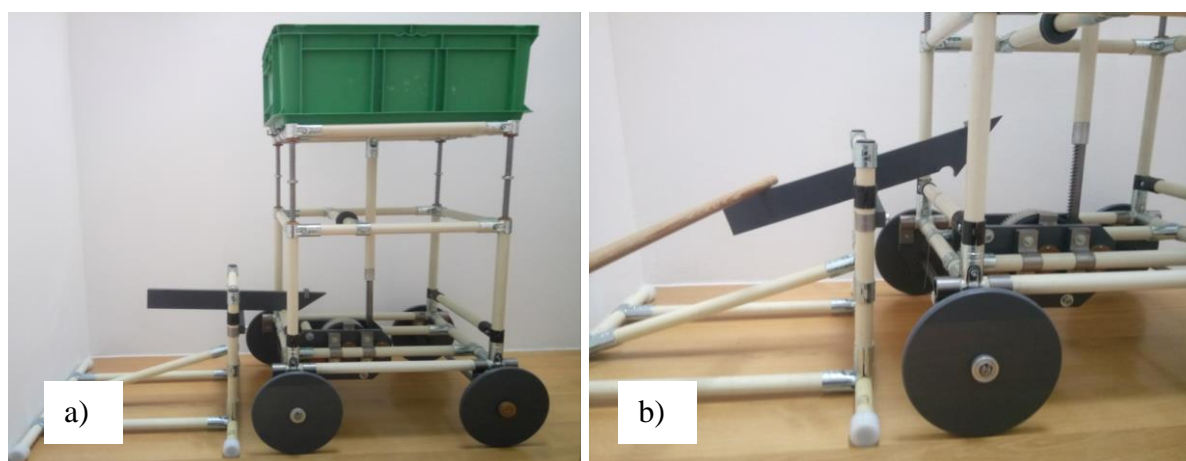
Konstrukční návrh záchytných mechanismů
